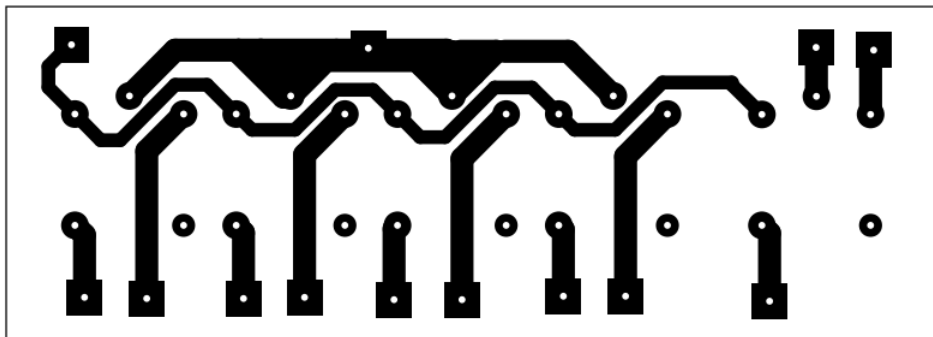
PCB voltiamperímetro [Fuente. El autor].
